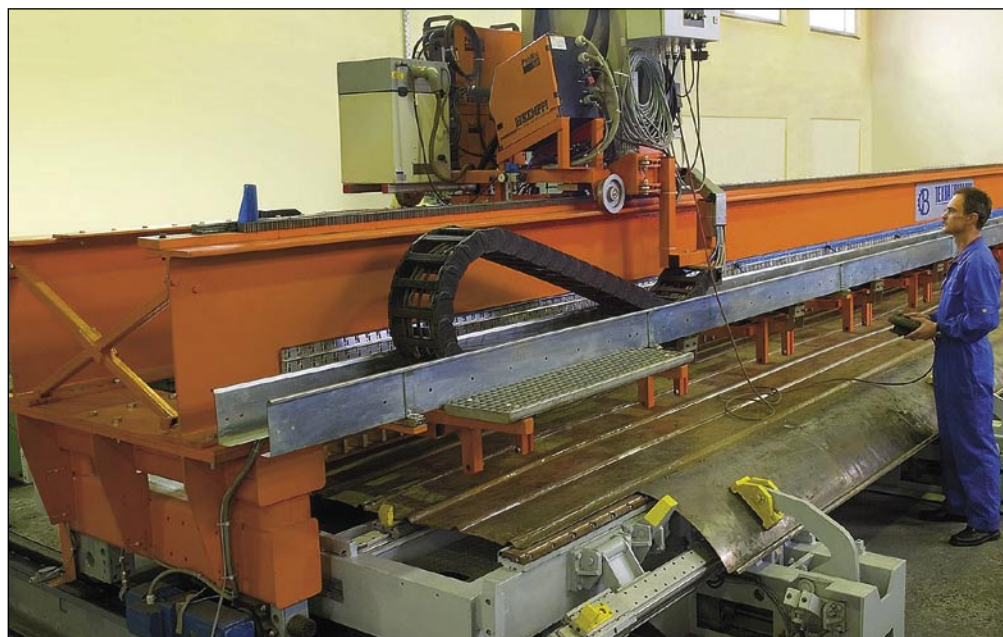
Универсальная установка автоматической сварки секций обшивки крыши пассажирских вагонов
